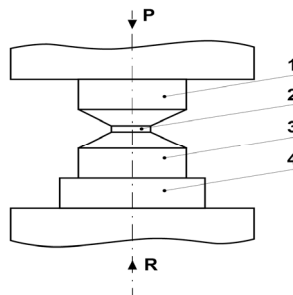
Схема установки: 1 - верхняя наковальня, 2 - образец, 3 – нижняя наковальня, 4 - вал редуктора
